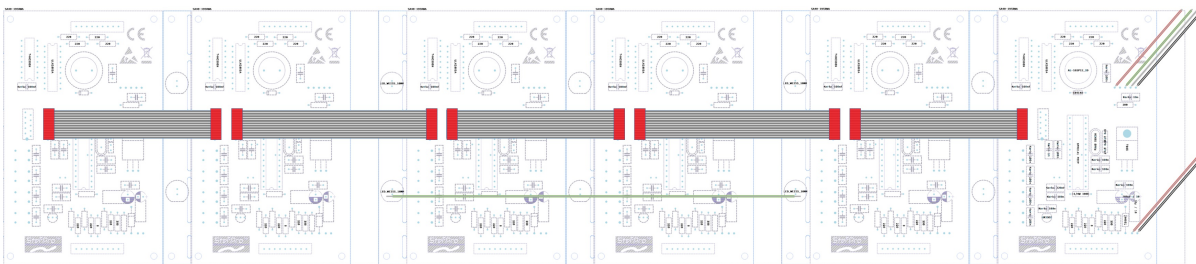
Stecker Beschreibung zum Modul SPP2490.0
